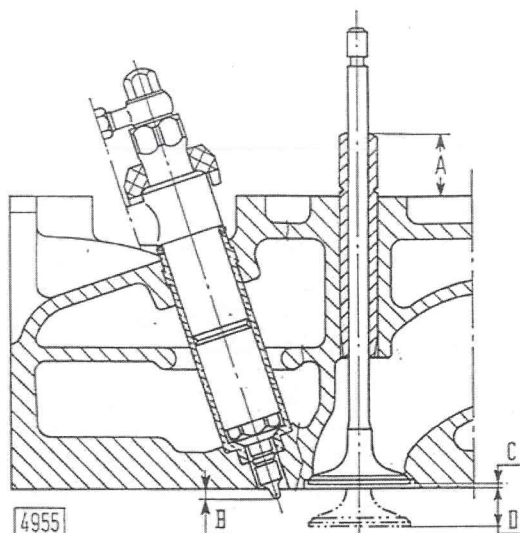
Posizioni corrette di montaggio delle valvole, guida valvole e iniettori nella testa cilindri.
